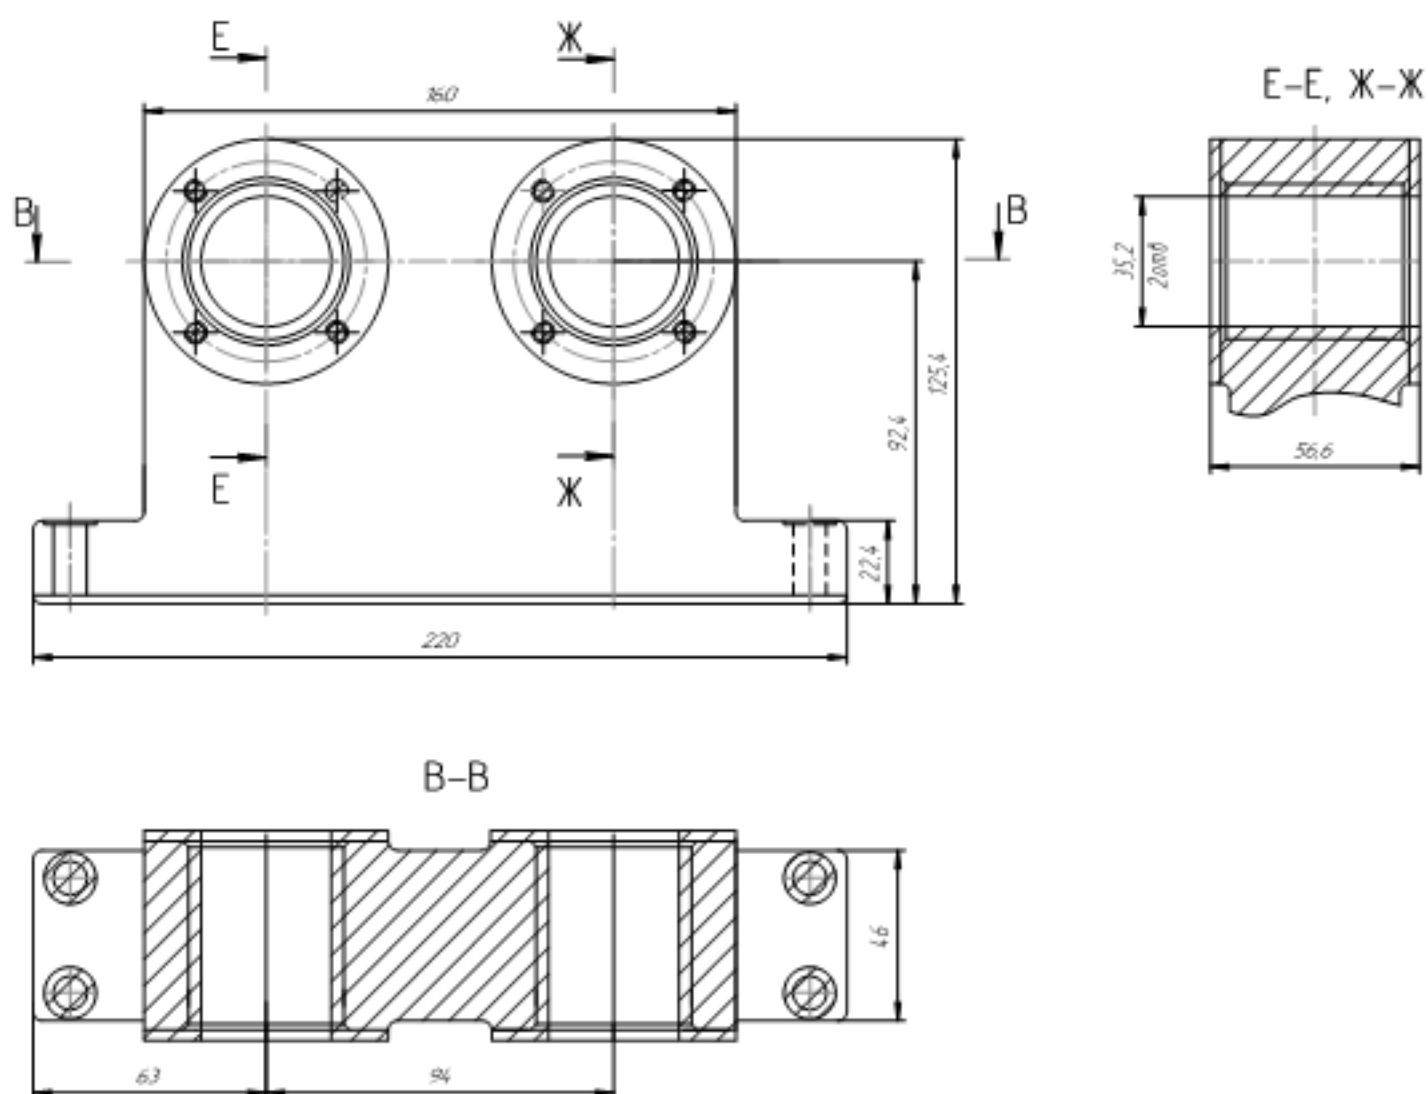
Заготовка виготовлена литтям в оболонкові форми
